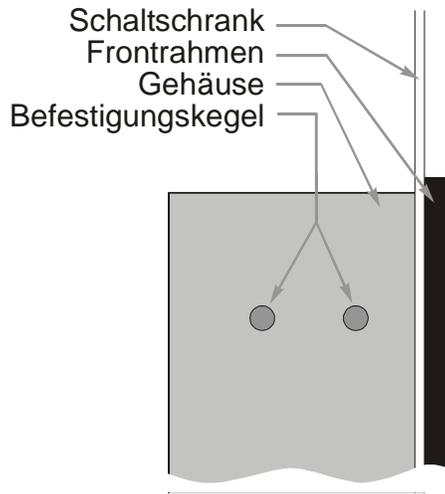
Seitenansicht - ohne Befestigungsklammer
